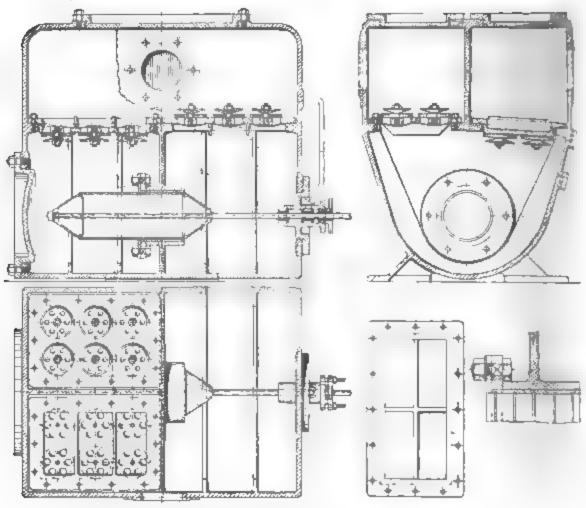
Luftpumpe mit Mönchskolben.
